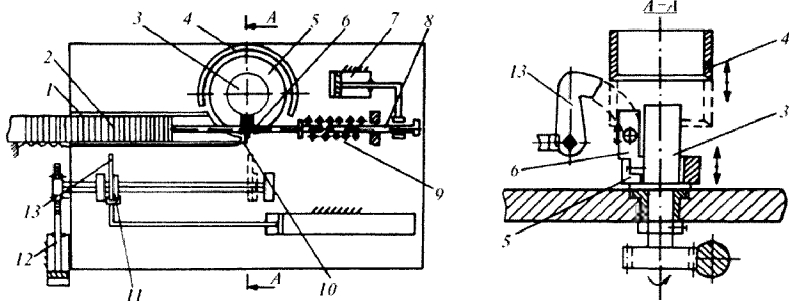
Схема механизма сборки заготовок лепестковых кругов:
